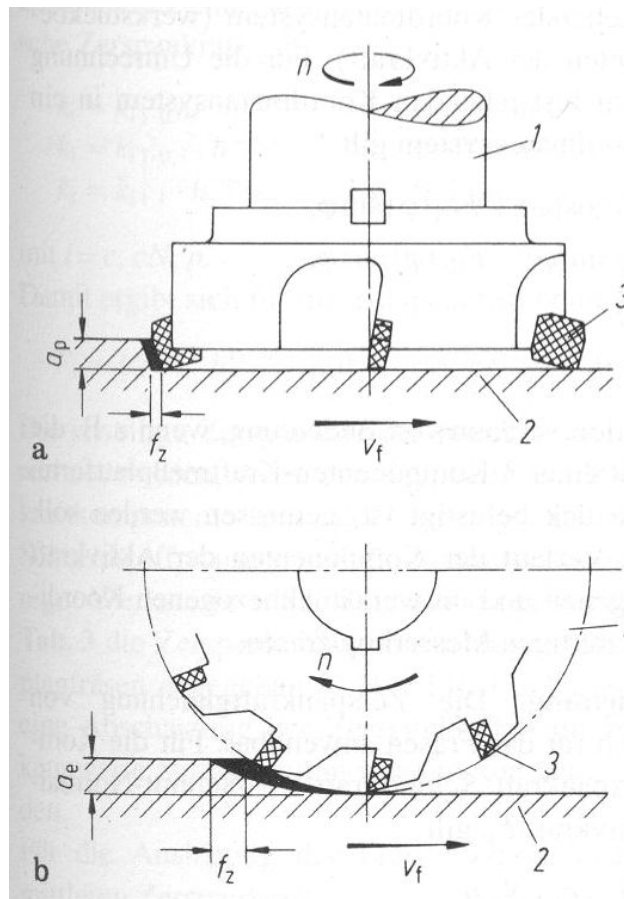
a, b. Gegenüberstellung: Stirnfräsen und Umfangsfräsen. a Stirnfräsen: Werkstückoberfläche erzeugt durch Nebenschneide; b Umfangsfräsen: Werkstückoberfläche erzeugt durch Hauptschneide; 1- Werkzeug, 2 - Werkstück, 3 - Schneide
